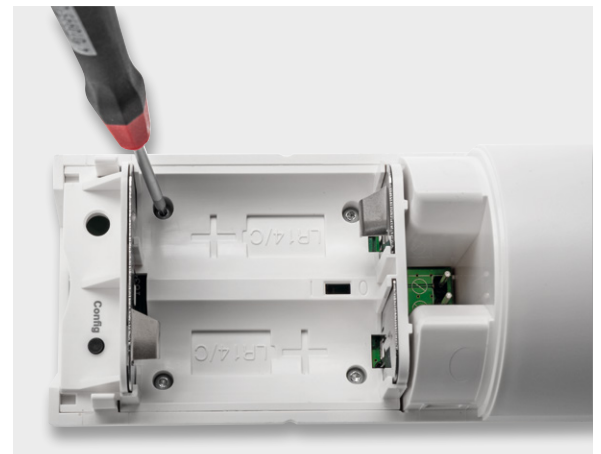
Das Batteriefach mit der aufgesetzten Hauptplatine wird mit vier Schrauben im Gehäuse befestigt.
